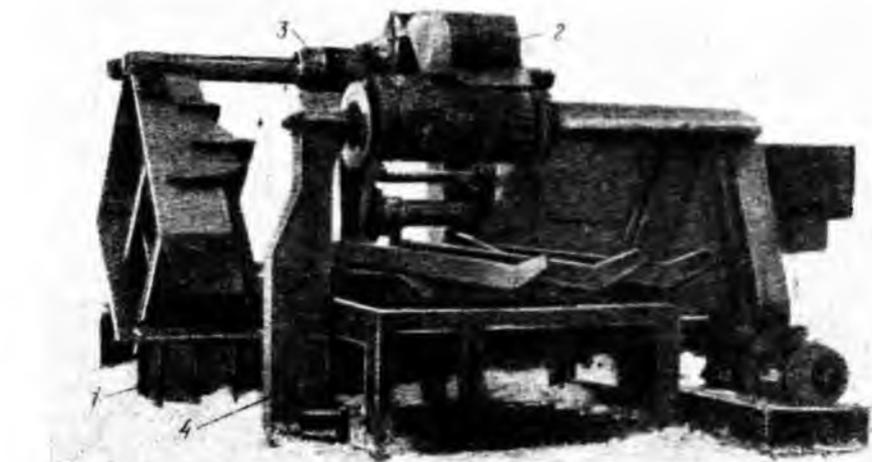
Общий вид окорочно-делительного станка: 1 — станок ДО-20; 2 — окорочная головка; 3 — электропривод; 4 — механизм центрирования, зажима и вращения кряжей
